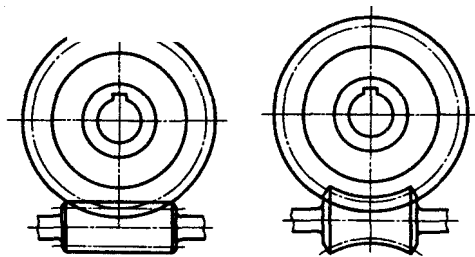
Схемы червячных передач с цилиндрическим (а) и глобоидным (б) червяками
